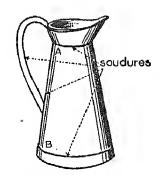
Ce broc en zinc comporte de nombreuses soudures.
